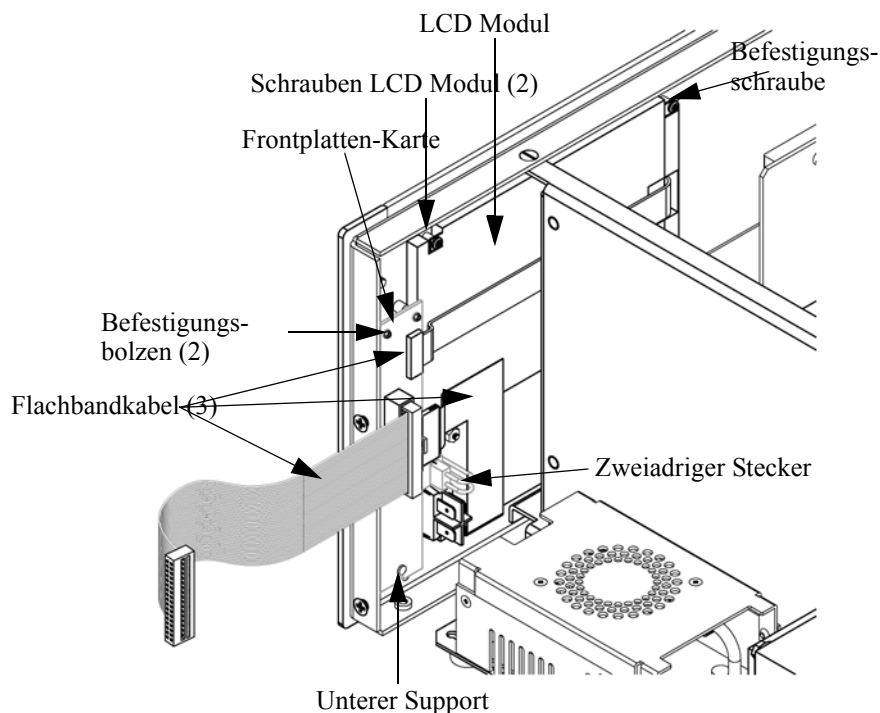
Frontplatten-Karte und LCD Modul tauschen
